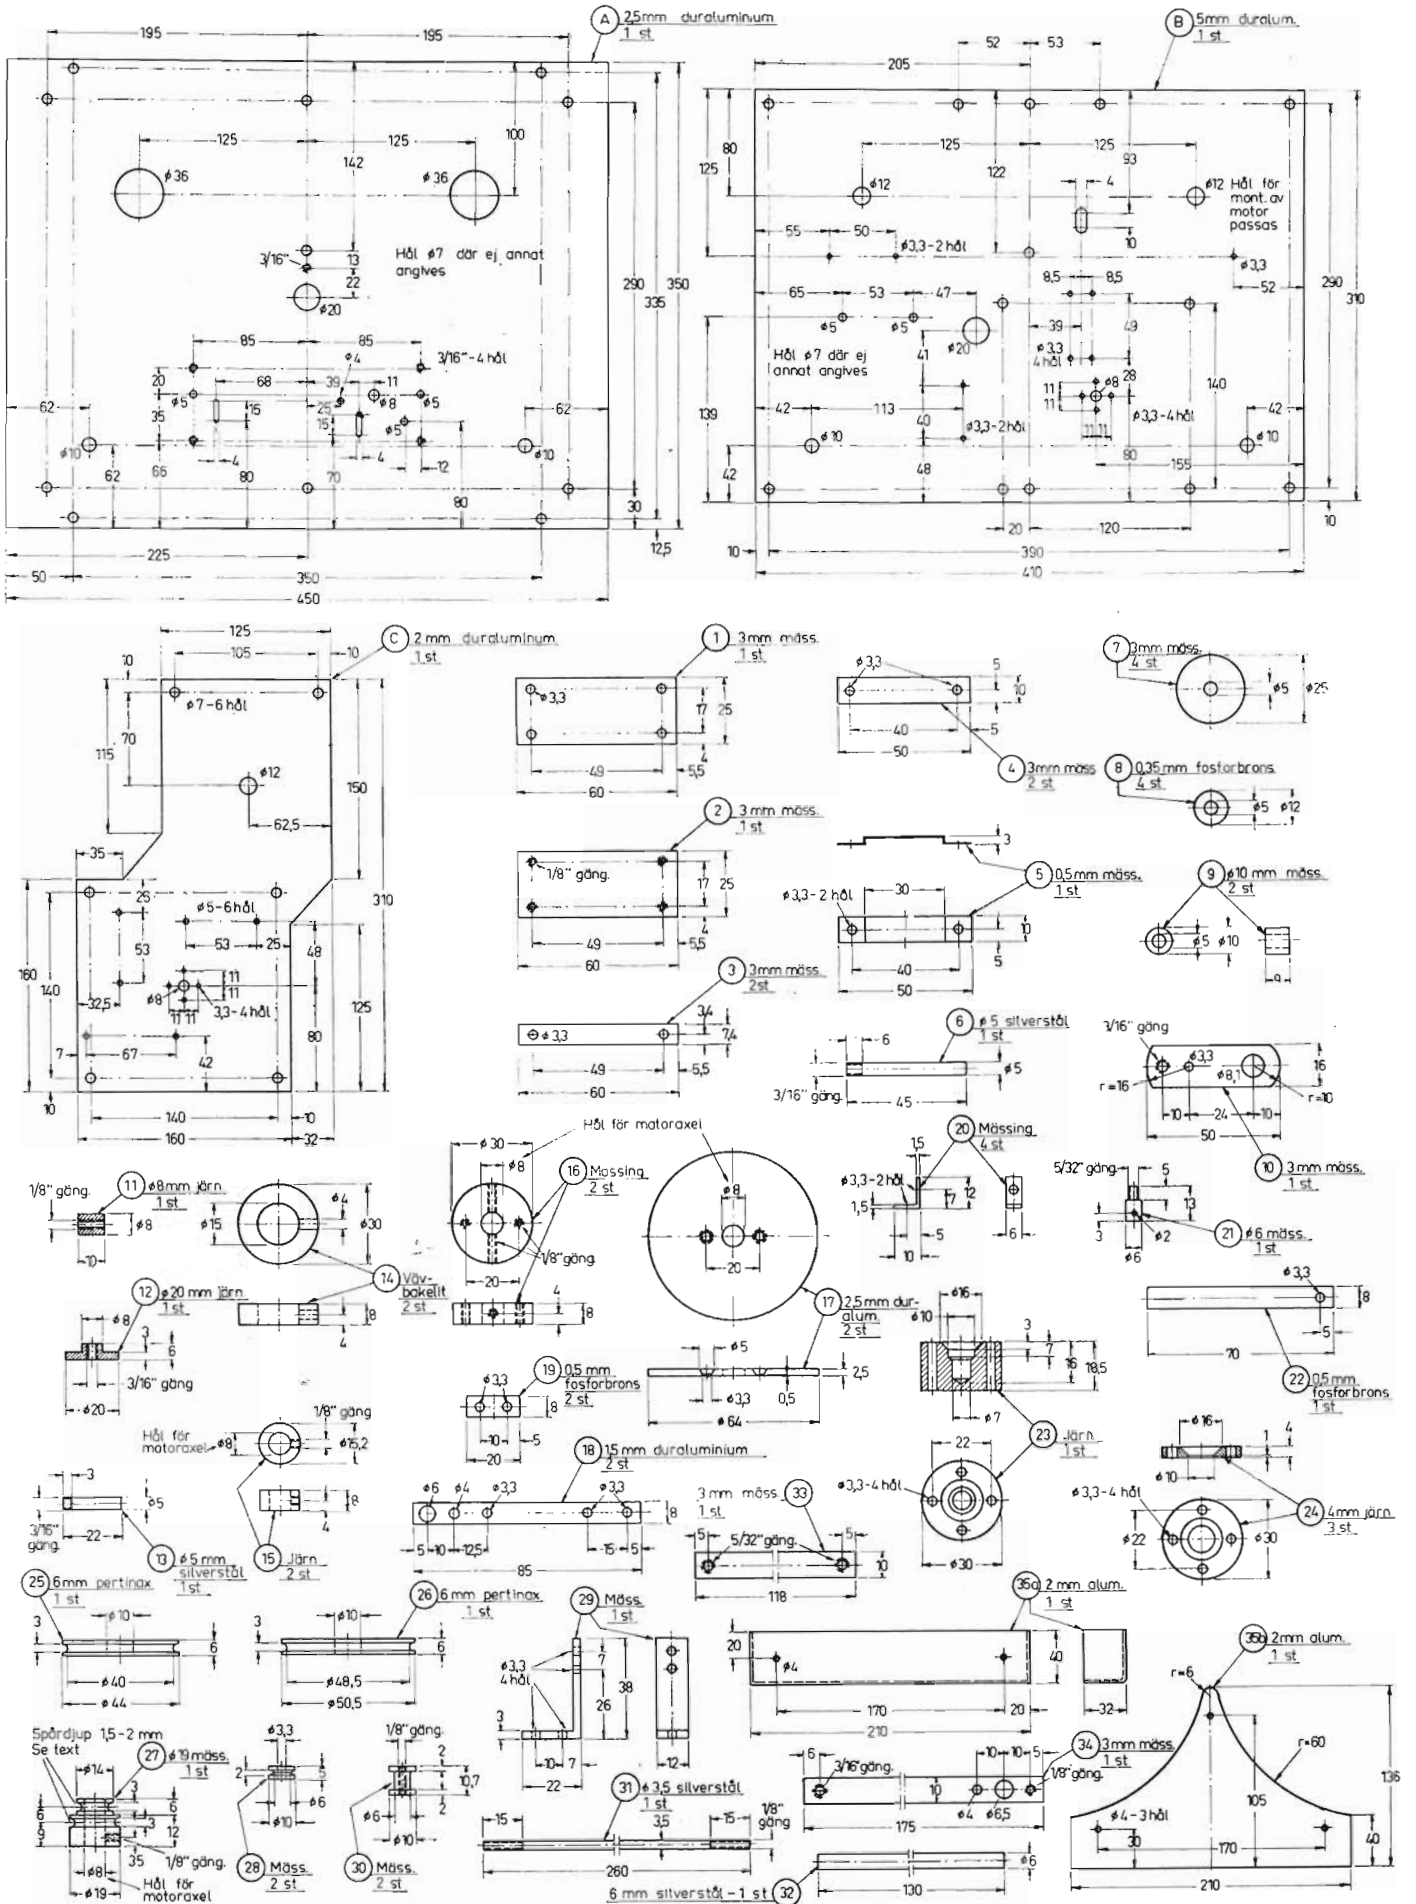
Måttskisser för de detaljer som ingår i bandspelarmekanismen.
